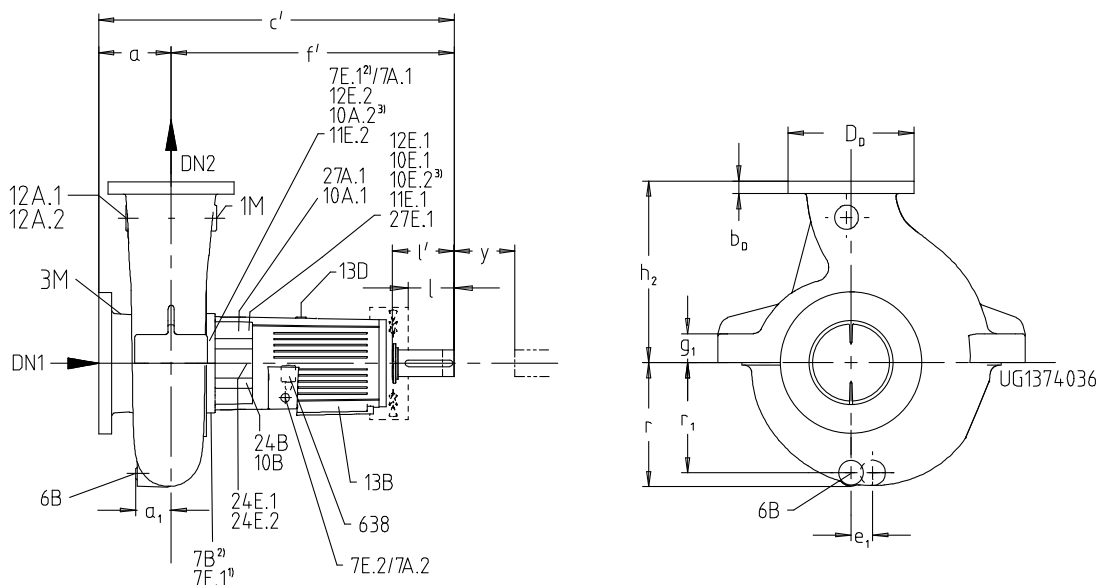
Габаритные/присоединительные размеры насоса, дополнительные типоразмеры
